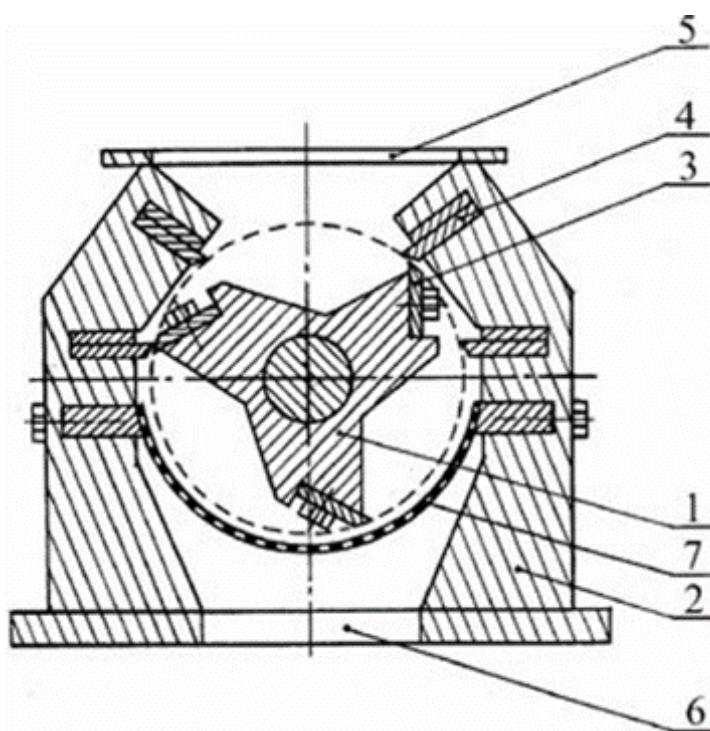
Роторно-ножовий подрібнювальний апарат подрібнювача Корсар Р-190 1 – ротор; 2 – корпус; 3 – рухомі ножі; 4 – нерухомі ножі; 5 – завантажувальний отвір; 6 – вивантажувальний отвір; 7 – сітка
